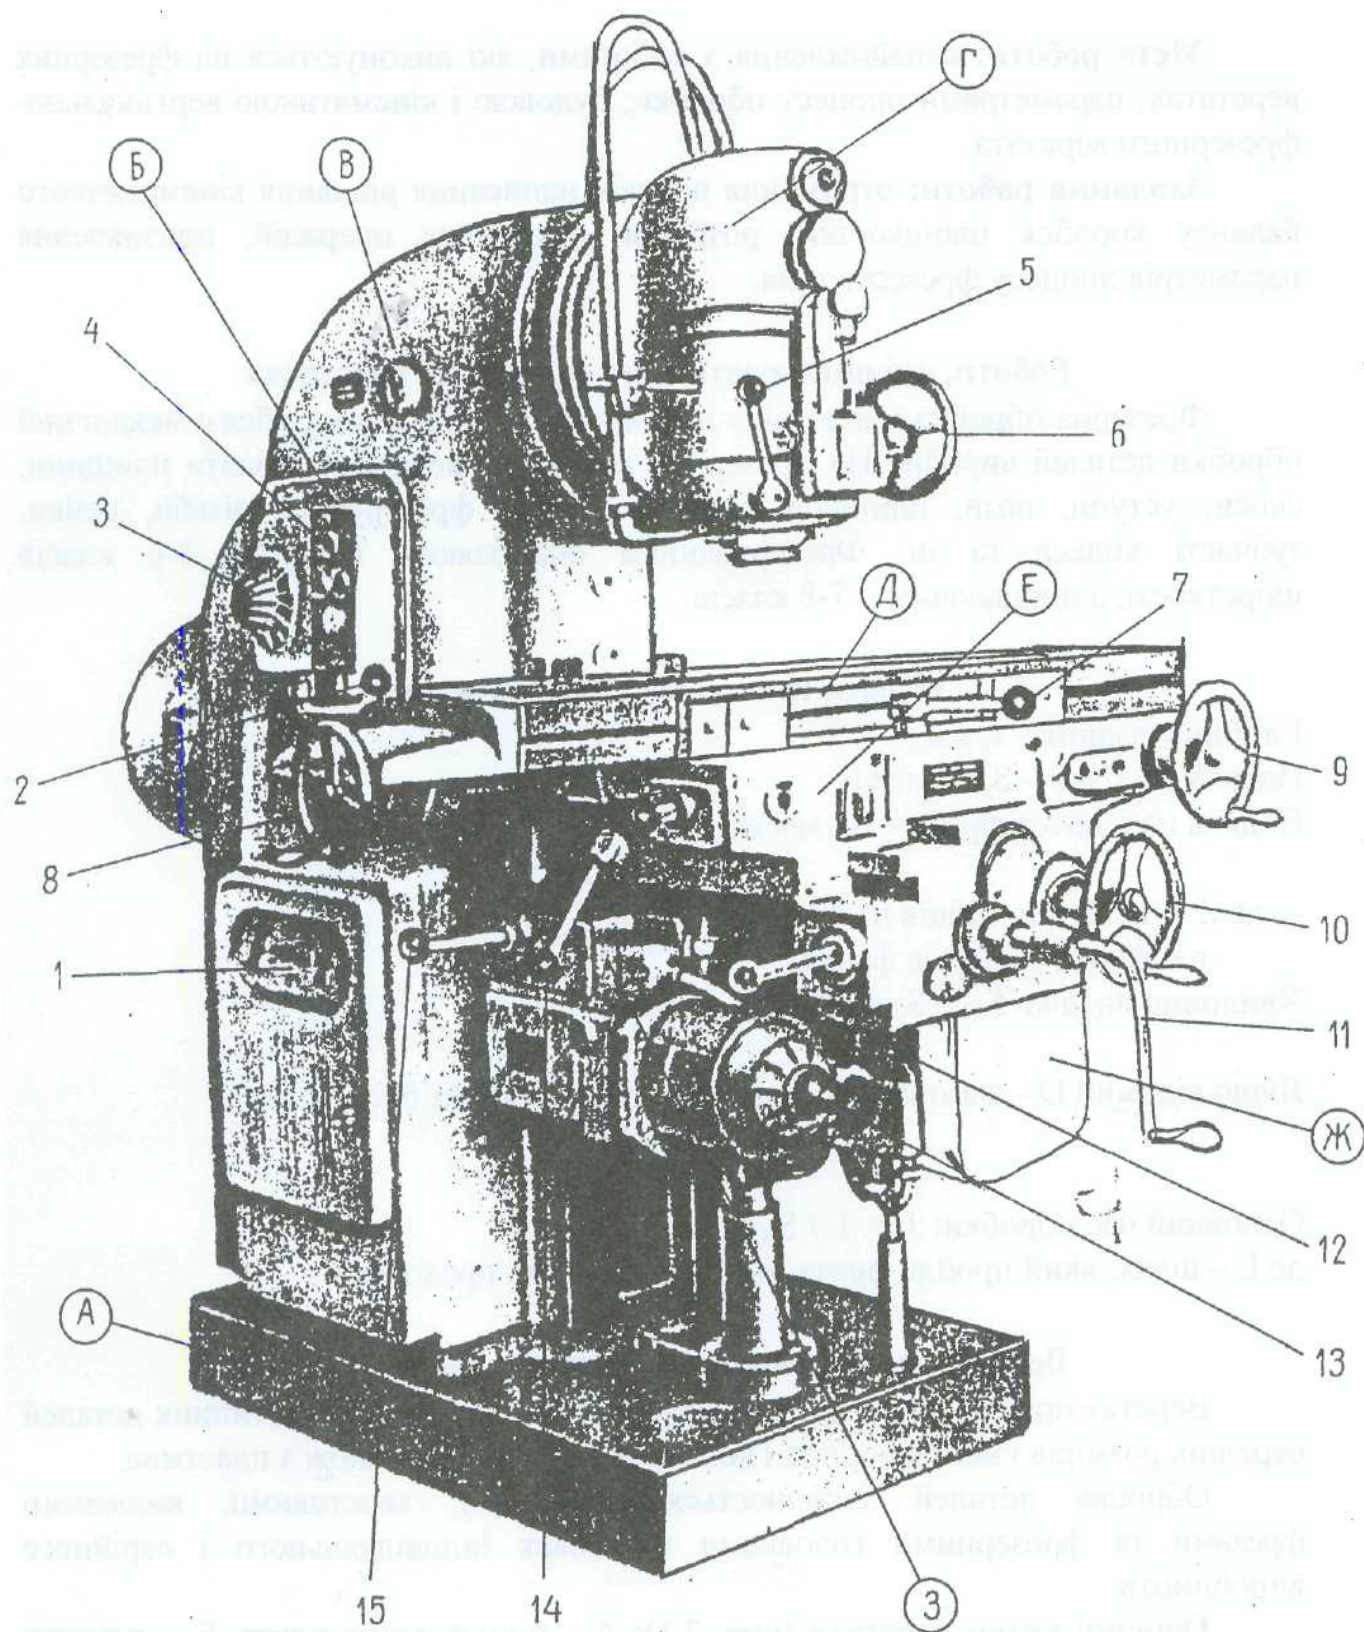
Вертикально-фрезерный верстат мод. 6Н12ПБ
